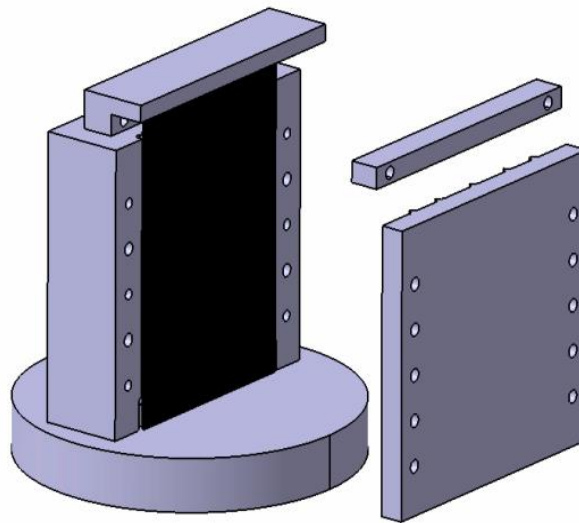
Diseño del útil CAI desarrollado con la posición de la probeta
